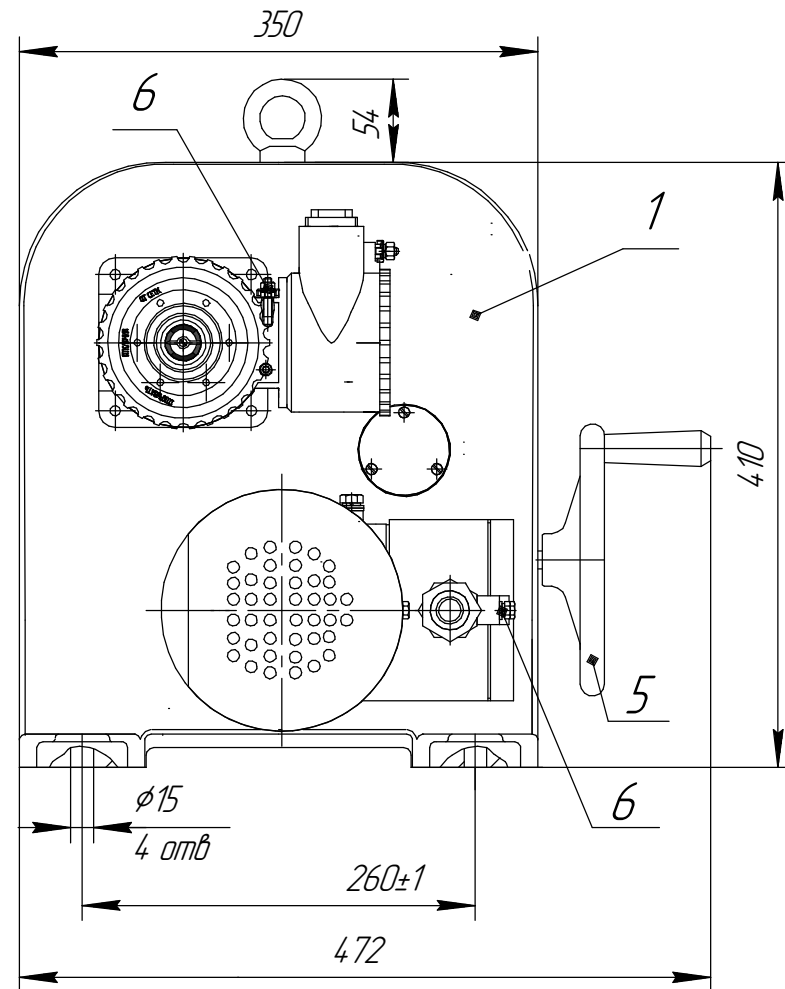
Общий вид, габаритные и присоединительные размеры механизма МЭОФ-ИВТ4 (МЭОФ-ИСТ4) группы 1000 с наружным квадратом выходного вала.
